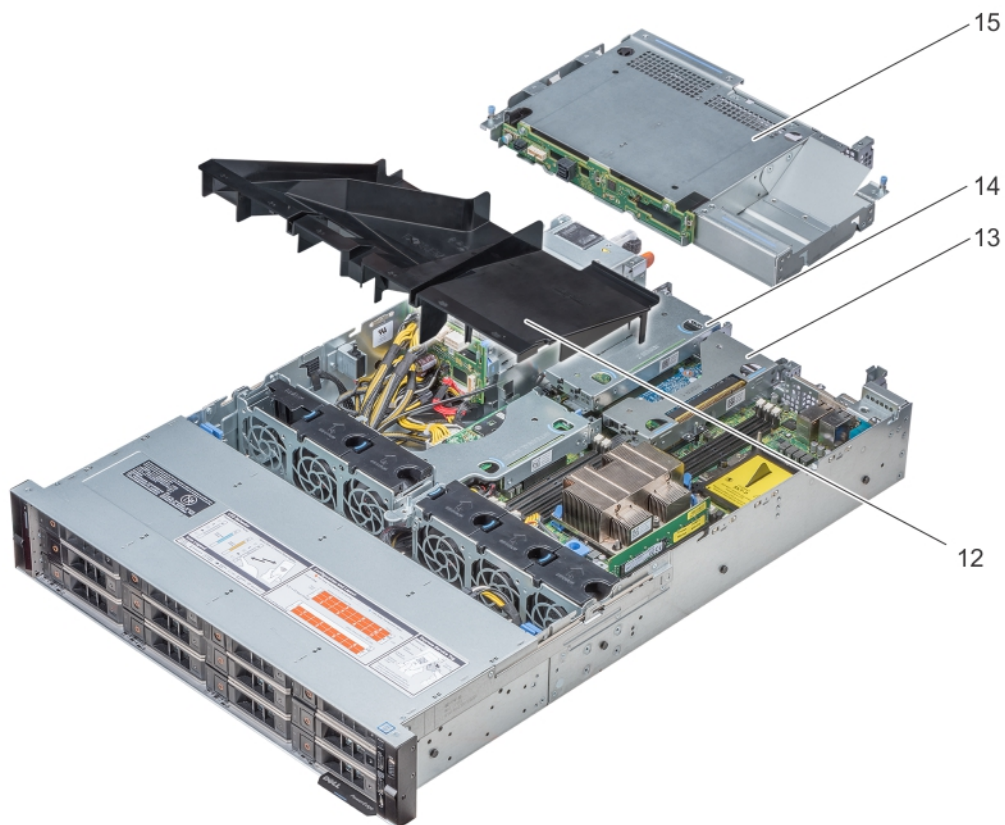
Das Systeminnere mit hinterem Laufwerksgehäuse
